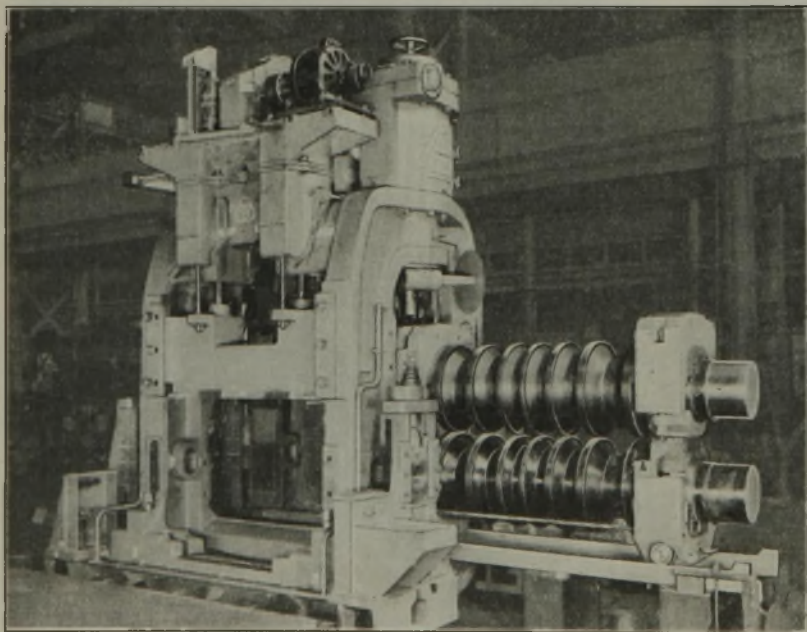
Walzenausbau mit Schienen und mit Rollen an den Einbaustücken.
